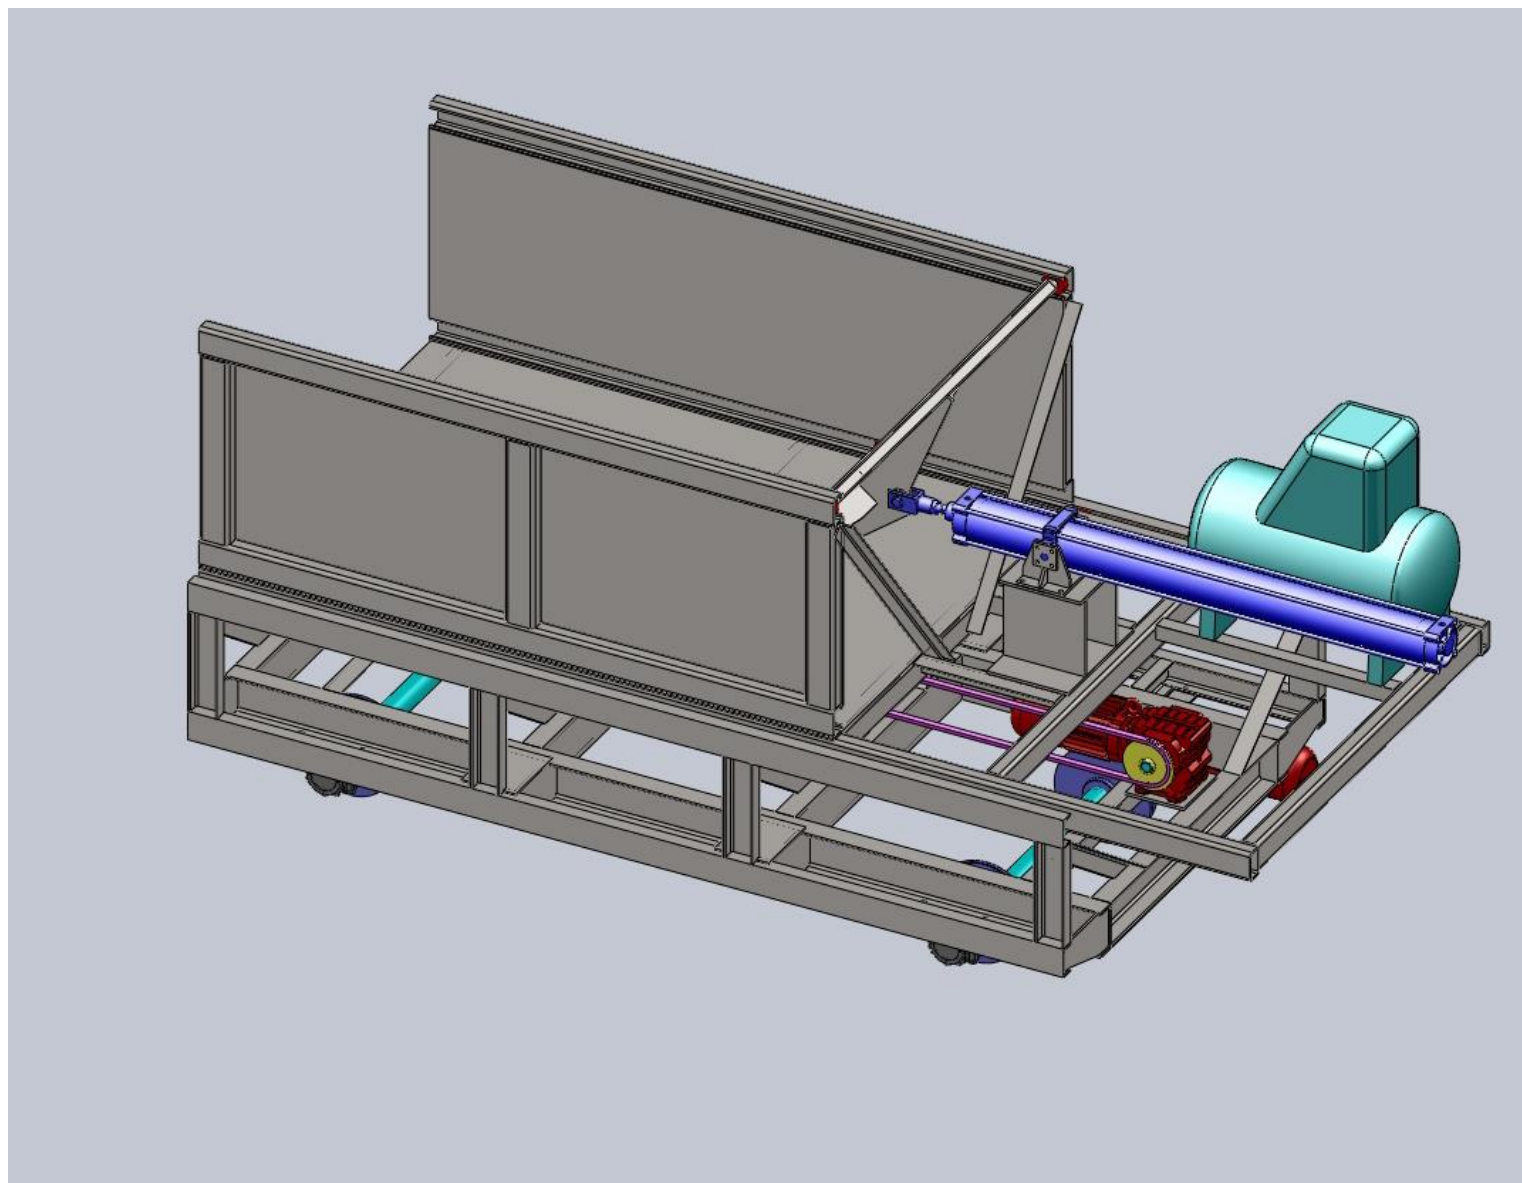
Общий вид загрузочной машины АНХ-МЗ-1400-2,0-500-1 конструкции «АНХ-Инжиниринг»
